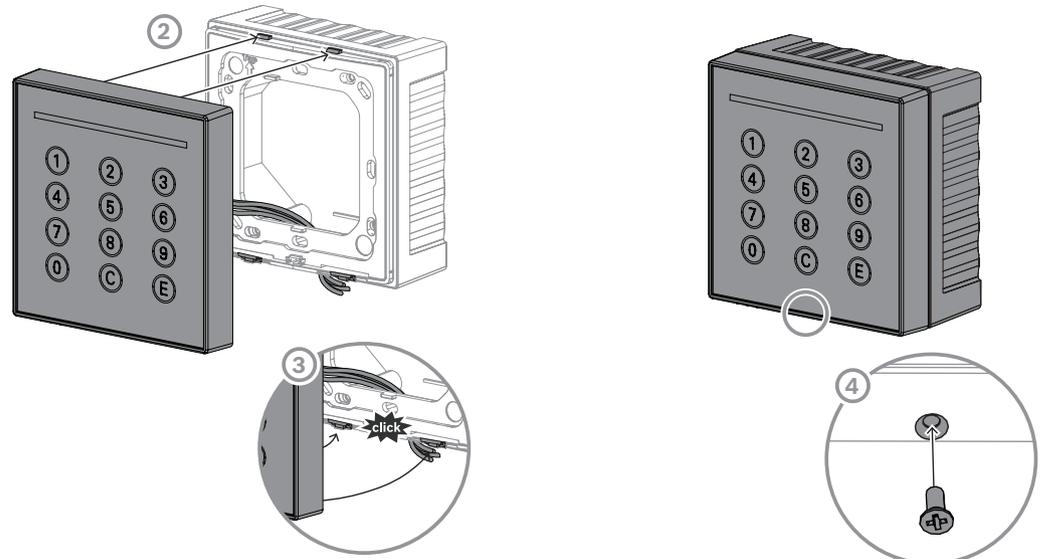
Raccordement et montage du module lecteur dans une installation en surface
